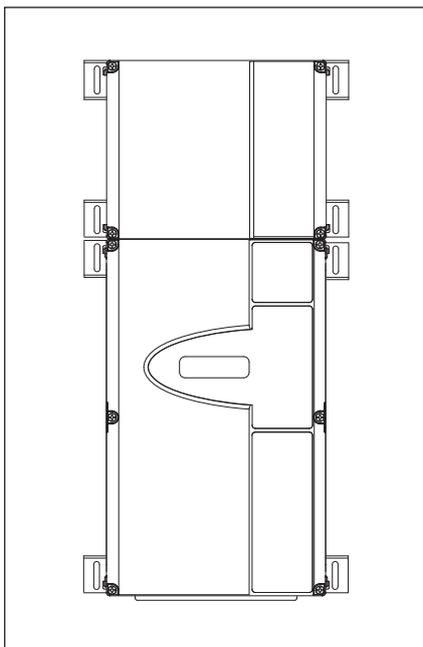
Steuerungsgehäuse und Erweiterungsgehäuse mit horizontal befestigten Montagefüßen
